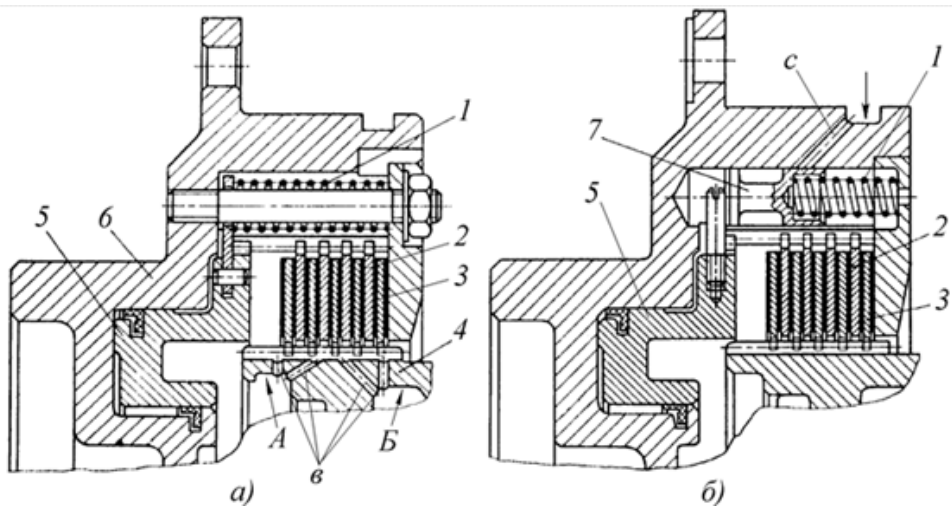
Дискові гальма, що працюють в маслі: 1 – поворотна пружина; 2 – сталевий диск; 3 – фрикційний диск з металокерамікою; 4 – маточина, що обертається; 5 – поршень; 6 – нерухомий корпус гальма; 7 – золотниковий клапан
